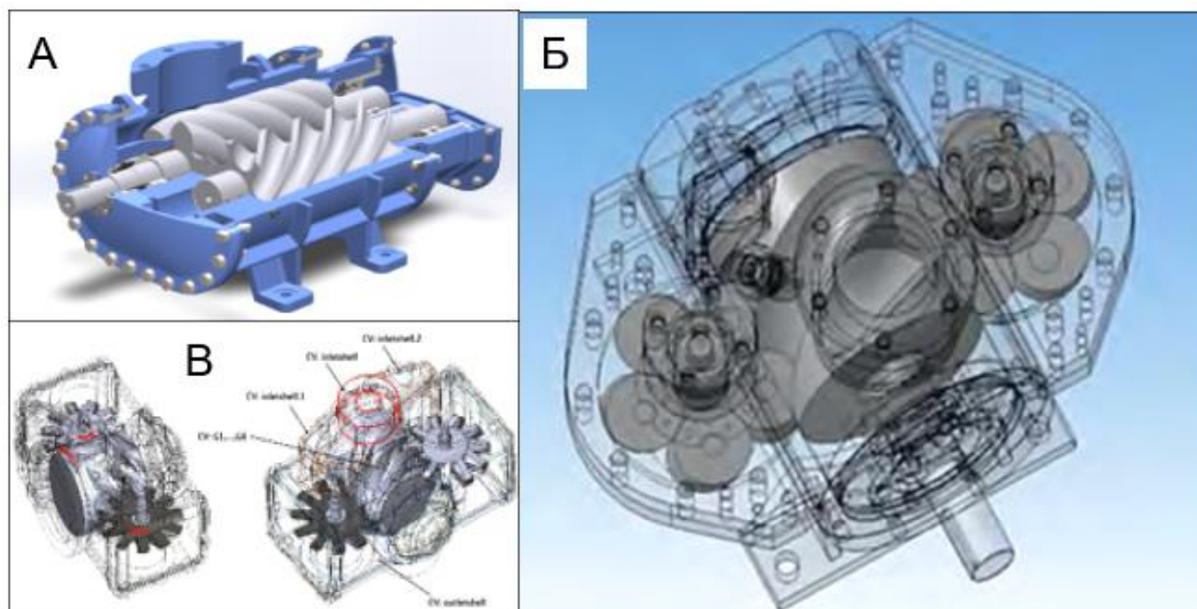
Винтовые компрессоры: а – двухвинтовой; б – однороторный с окружной формой зуба отсекаателя; в – однороторный с прямоугольной формой зуба отсекаателя
